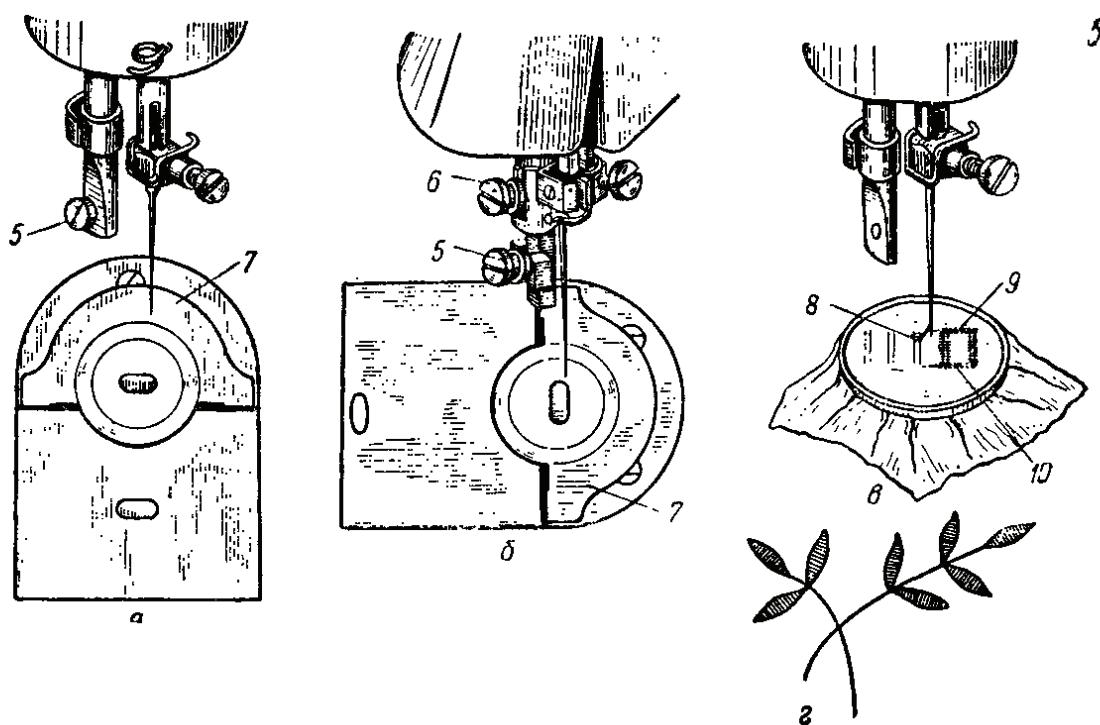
Подготовка машины к вышивке, выполнение вышивки „ришелье“ и гладьевых застилок:
